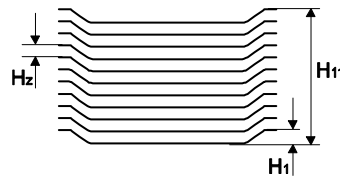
Altezza di pila intermedia H_z per 11 pezzi di stoviglie
